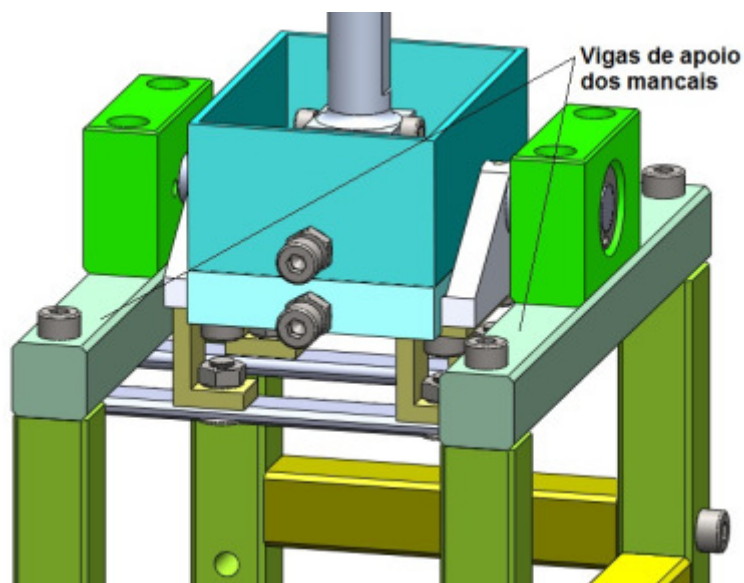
Posição das vigas de apoio dos mancais de oscilação da cuba, no dispositivo.
